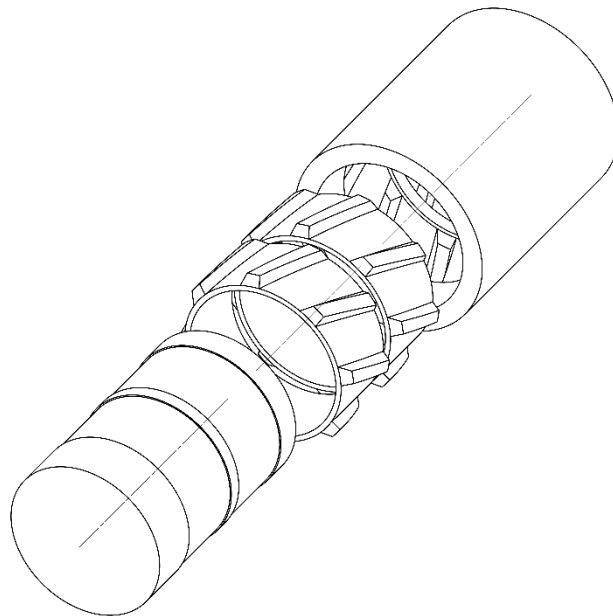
Разнесённая схема сборки для профиля 8
